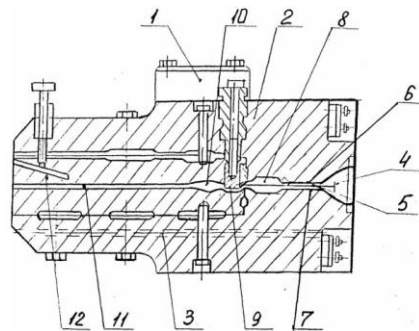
Вертикальний розріз екструзійної головки
